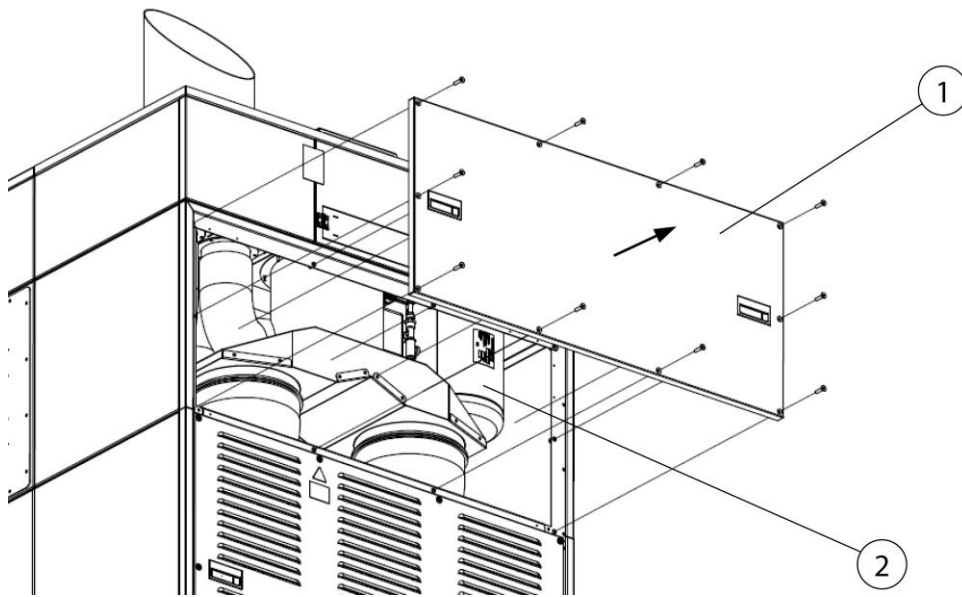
Доступ к резервуару для сжатого воздуха и пневматическому предохранительному клапану
